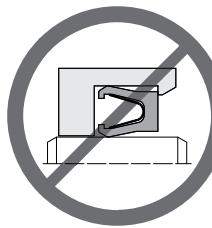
Неправильная установка ступенчатой посадочной канавки
